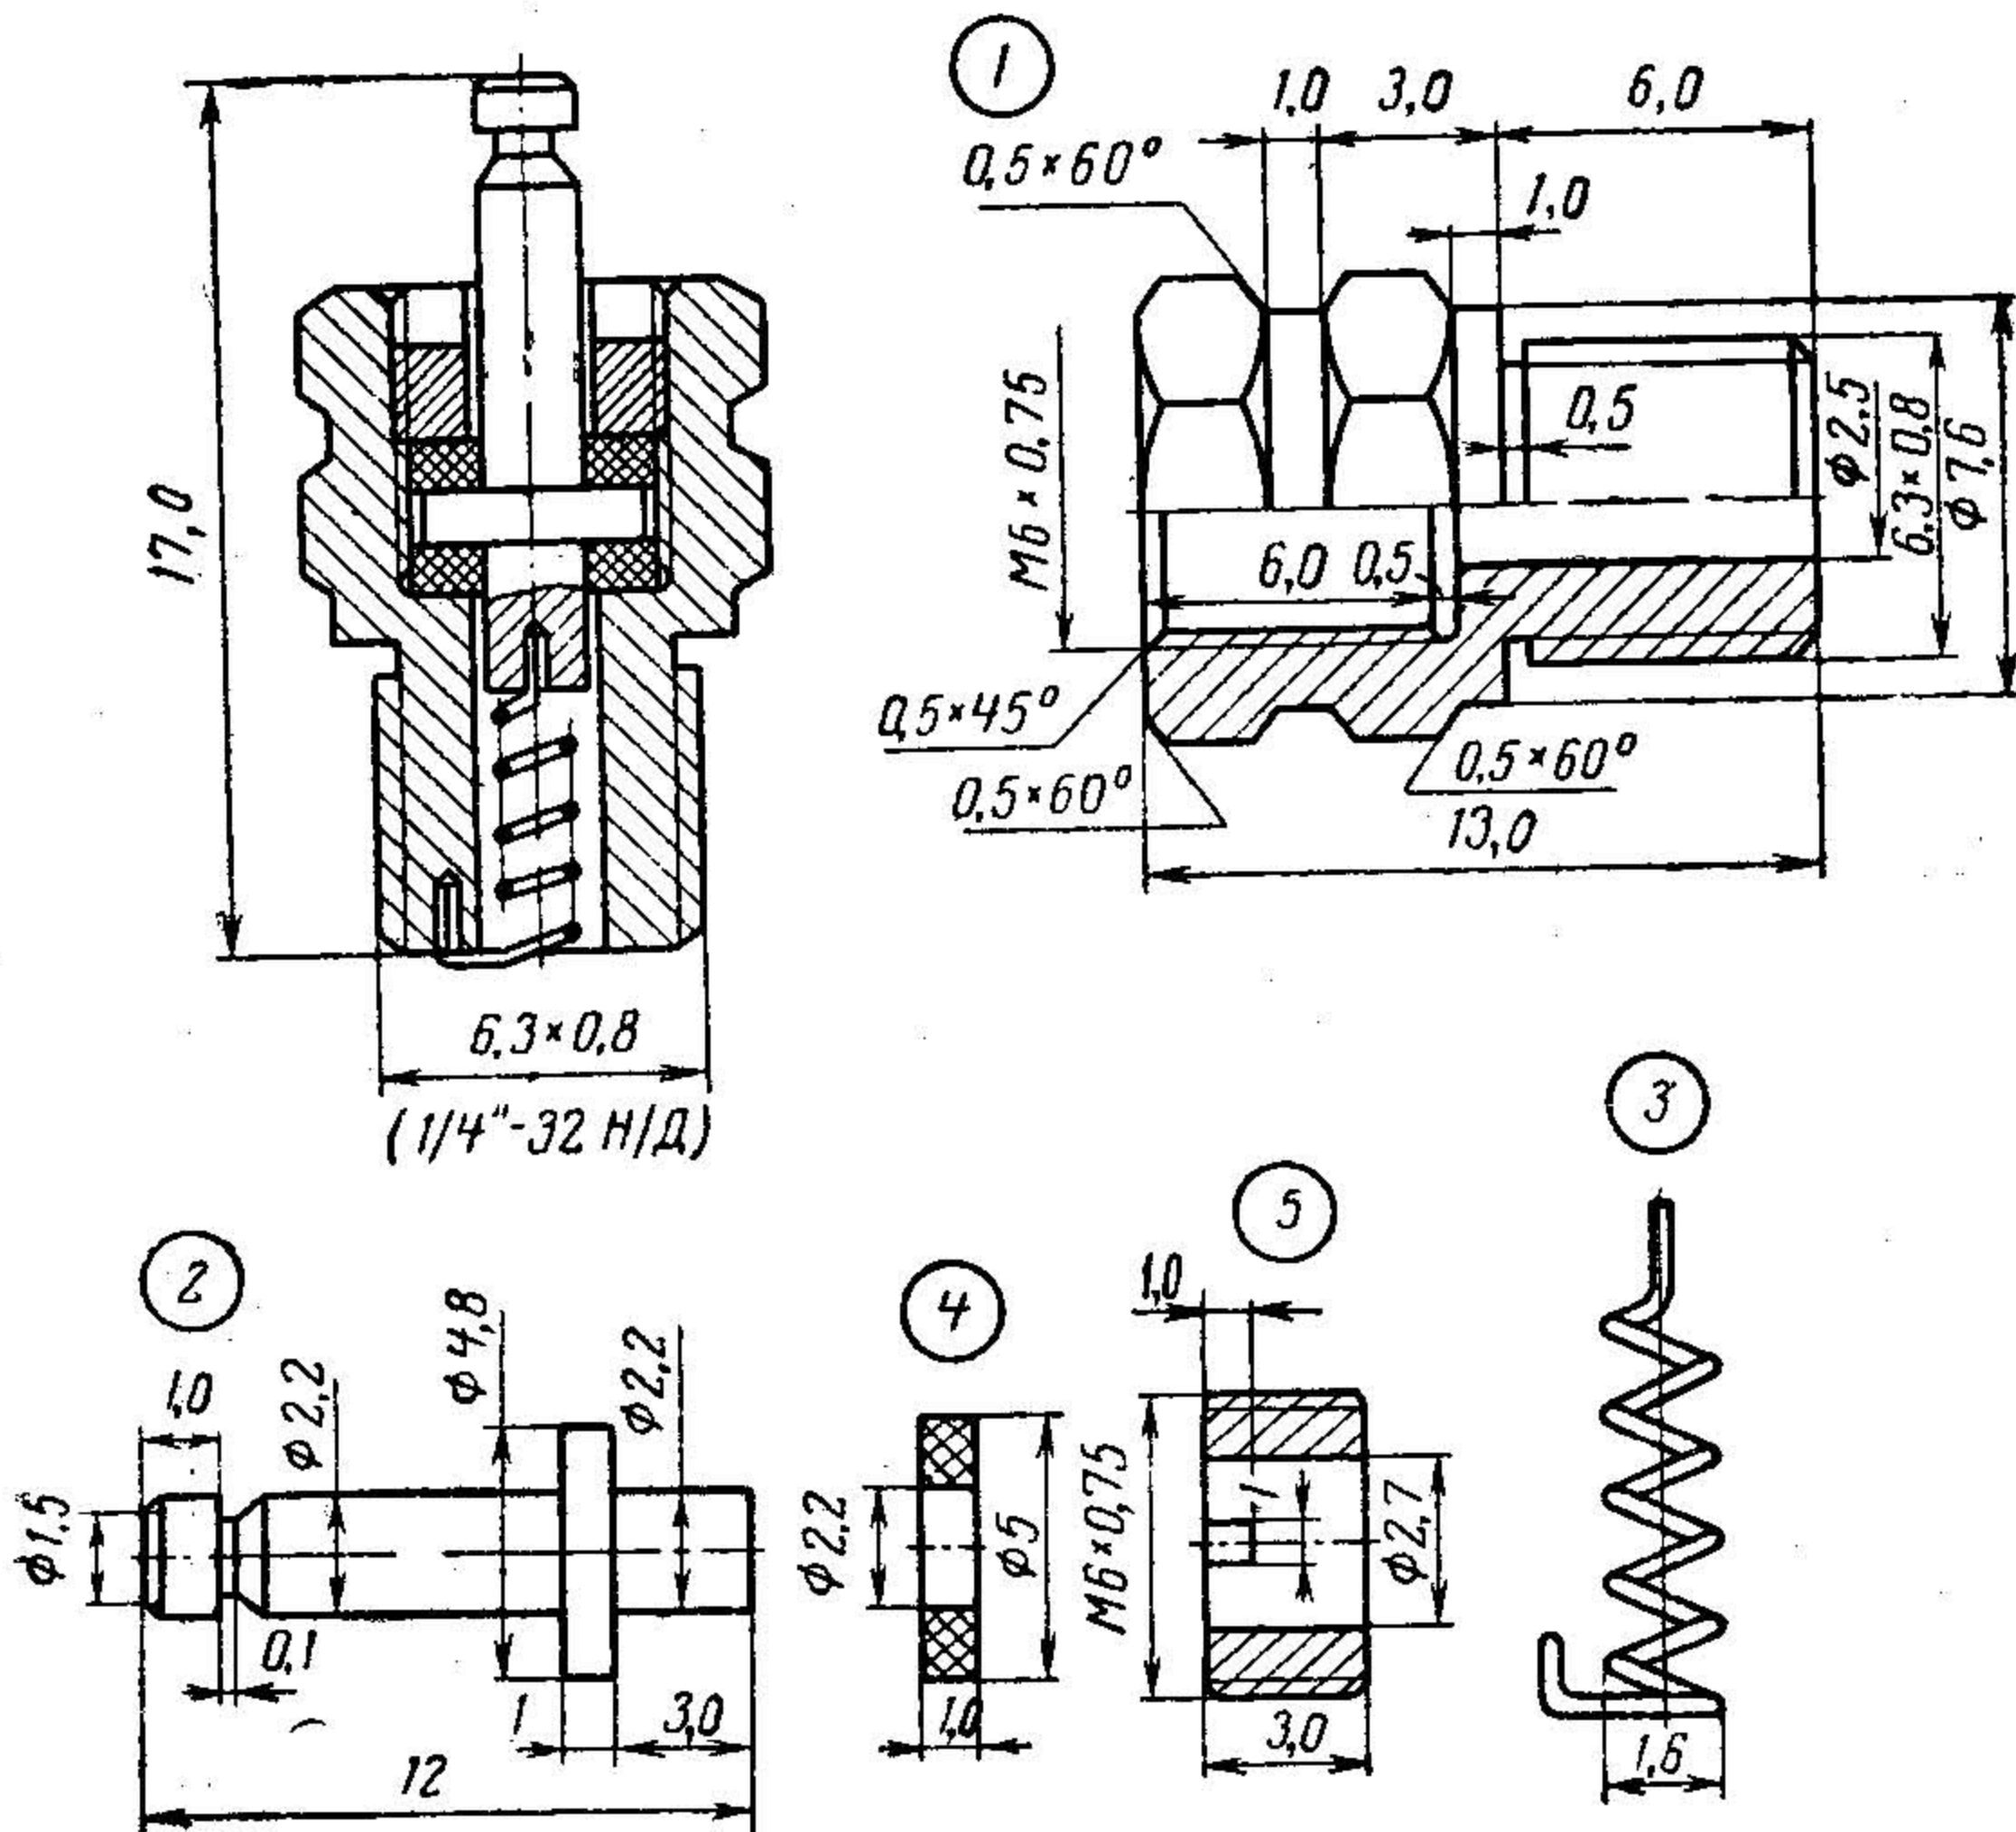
Разборная калильная свеча: 1 — корпус свечи; 2 — электрод; 3 — спираль; 4 — прокладка; 5 — гайка
